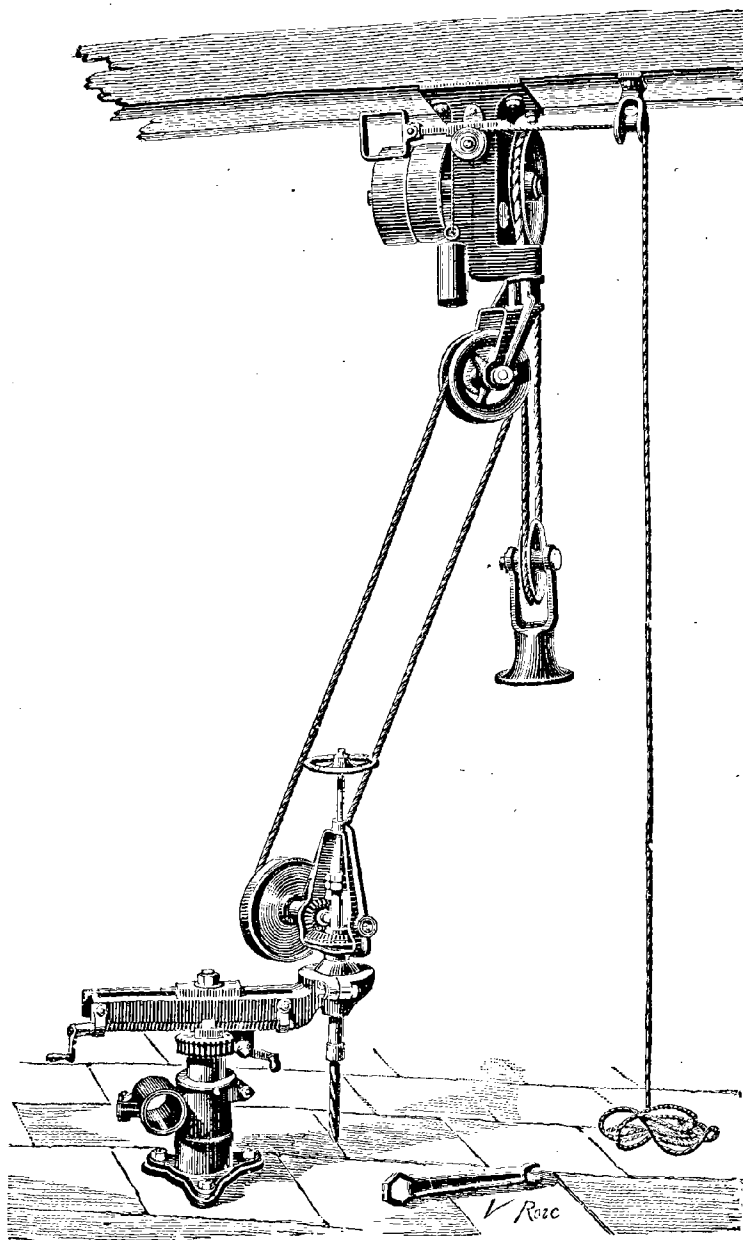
Machine à percer radiale universelle portable Thorne.
